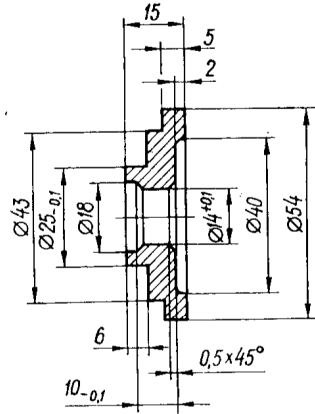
Оправка для запрессовки манжеты полуоси и поворотного кулака и выпрессовки внутренних подшипников колесного редуктора
